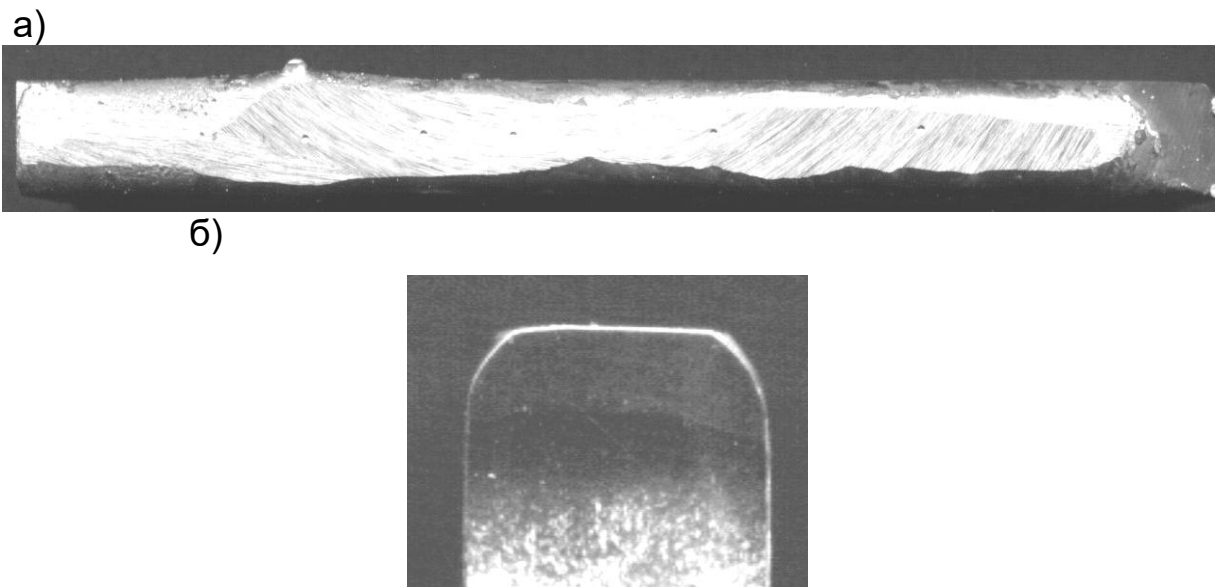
Поверхность (а) и поперечный шлиф (б) образца, наплавленного порошком ПР-НХ16СР3 методом плазменной наплавки
